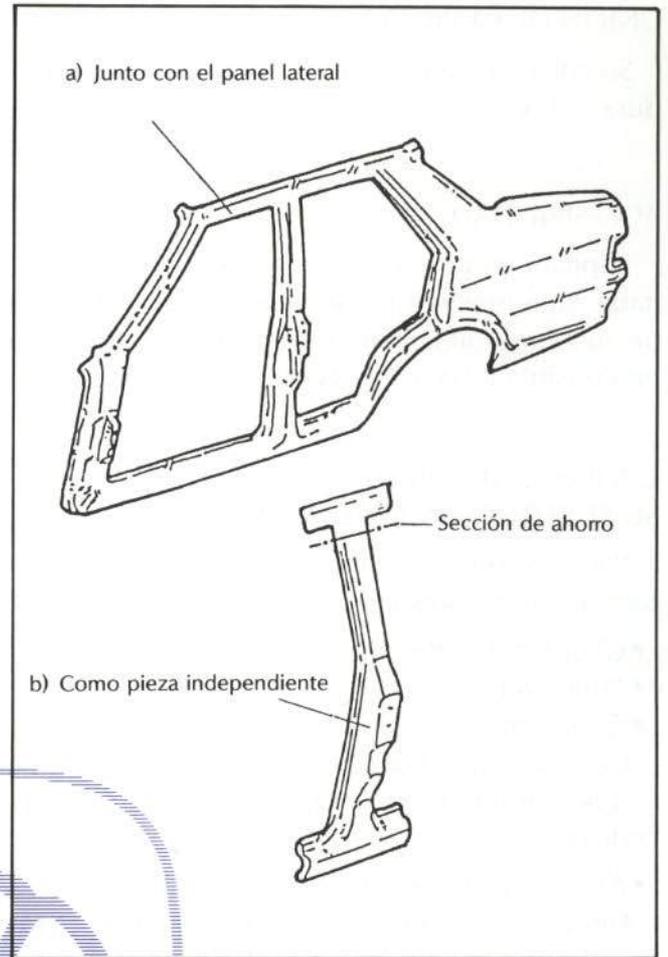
Comercialización y sección de ahorro del pilar central.
